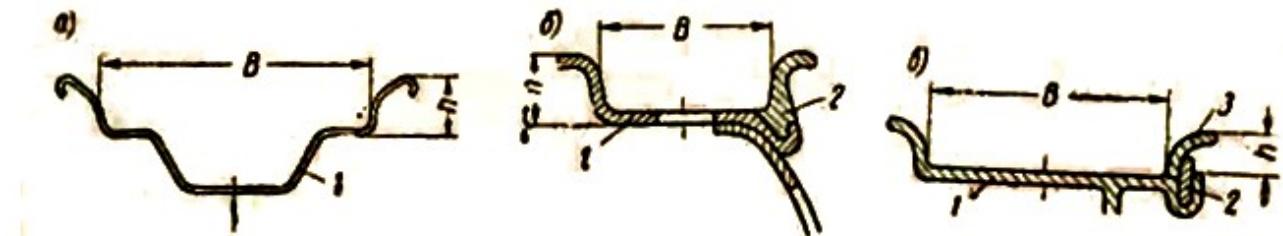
Обода колес: B - ширина обода; h - высота закраины; 1 - обод; 2 - съемное разрезное бортовое кольцо, 3 - запорное бортовое кольцо
